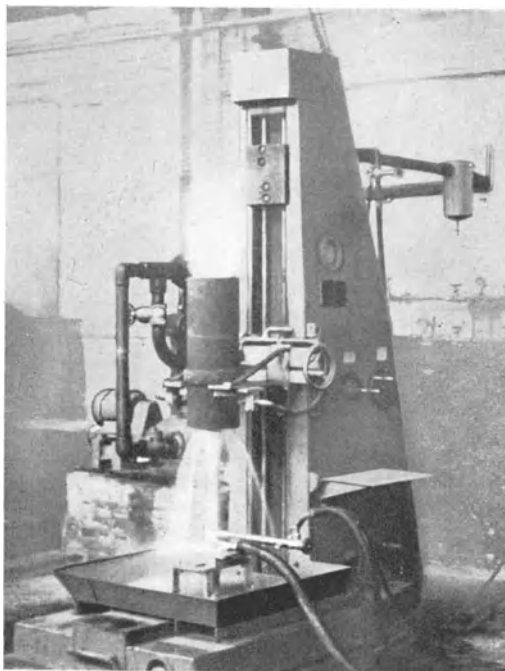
Innenhärtung einer Zylinderbüchse nach dem Umlauf-Vorschubverfahren auf einer Senkrechthärtemaschine.
